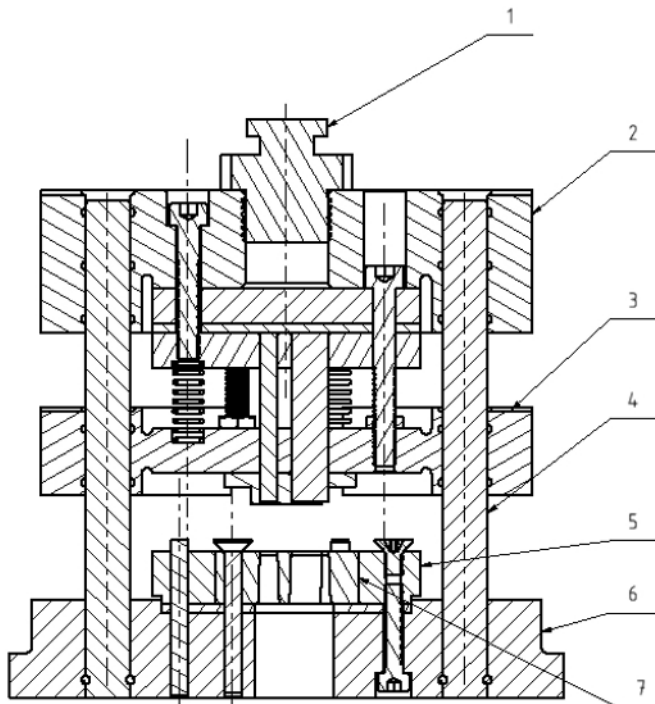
Ausstanzwerkzeug mit Lochschnitt
